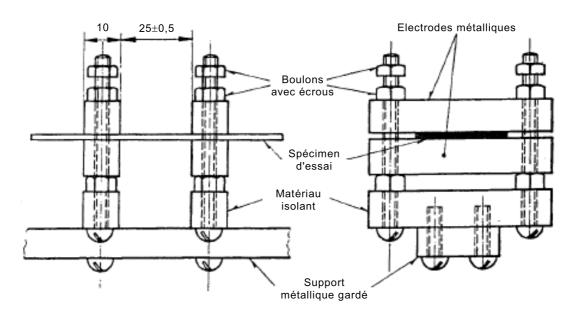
Arrangement de spécimen d'essai pour tubes et tiges
